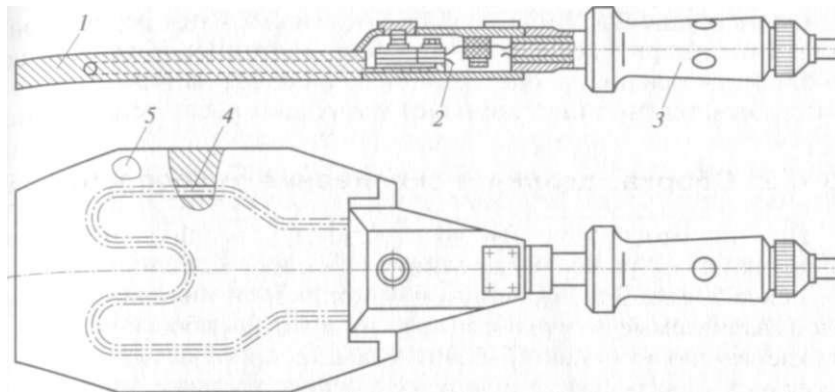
Электронагревательный инструмент для сварки встык:
